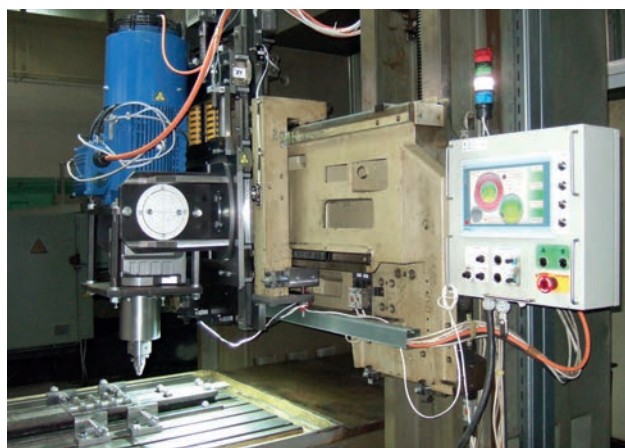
Общий вид установки фрикционной сварки ERNEST
